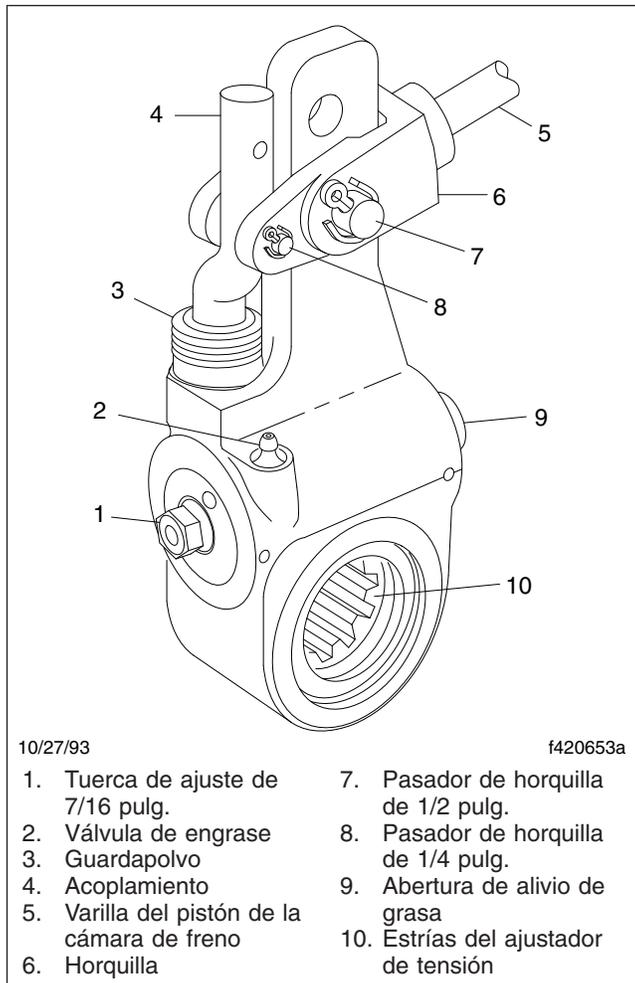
, Válvula de engrase del ajustador de tensión automático Haldex
